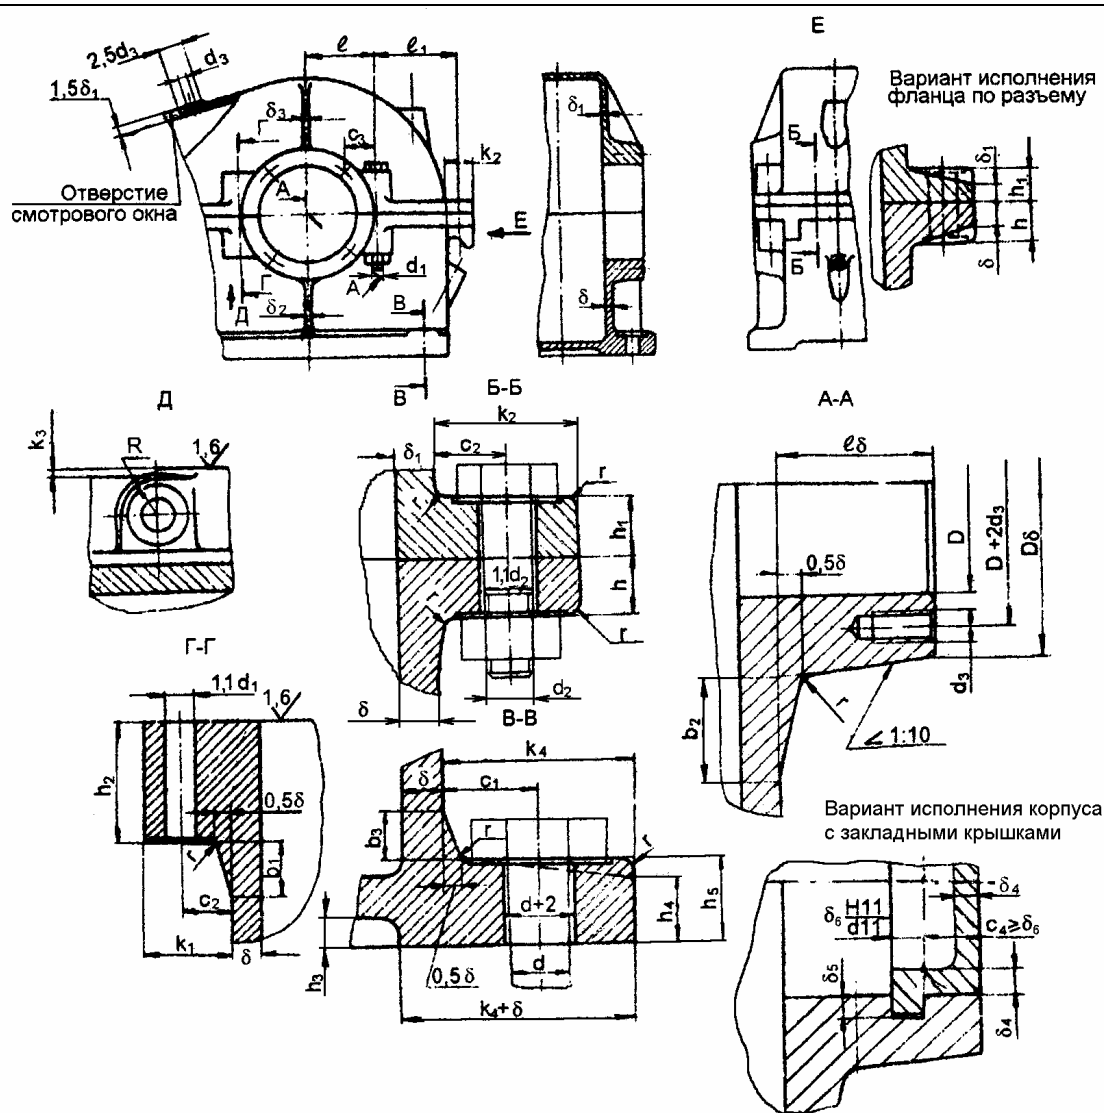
Варианты крепления крышки к корпусу редуктора
